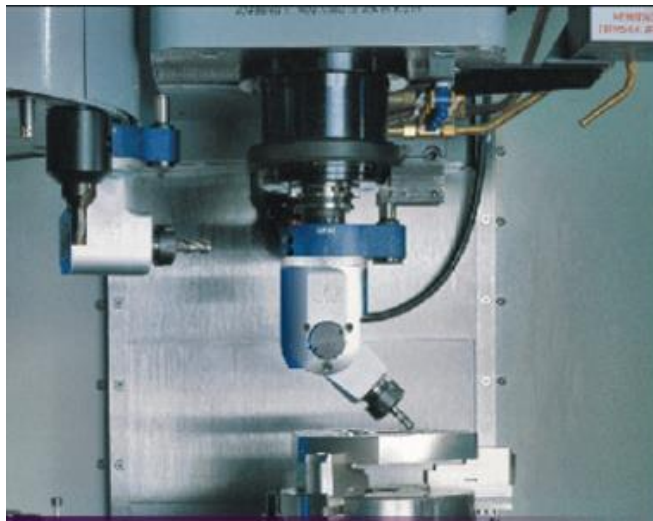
Cabezal universal para centro de mecanizado montado al husillo de una máquina.
